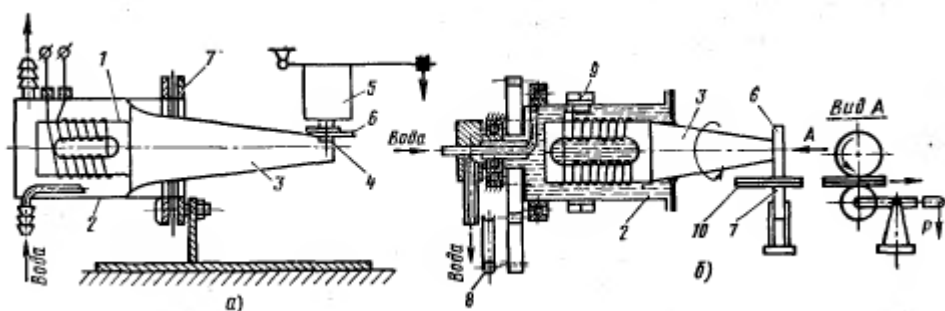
Схема установки для сварки ультразвуком
